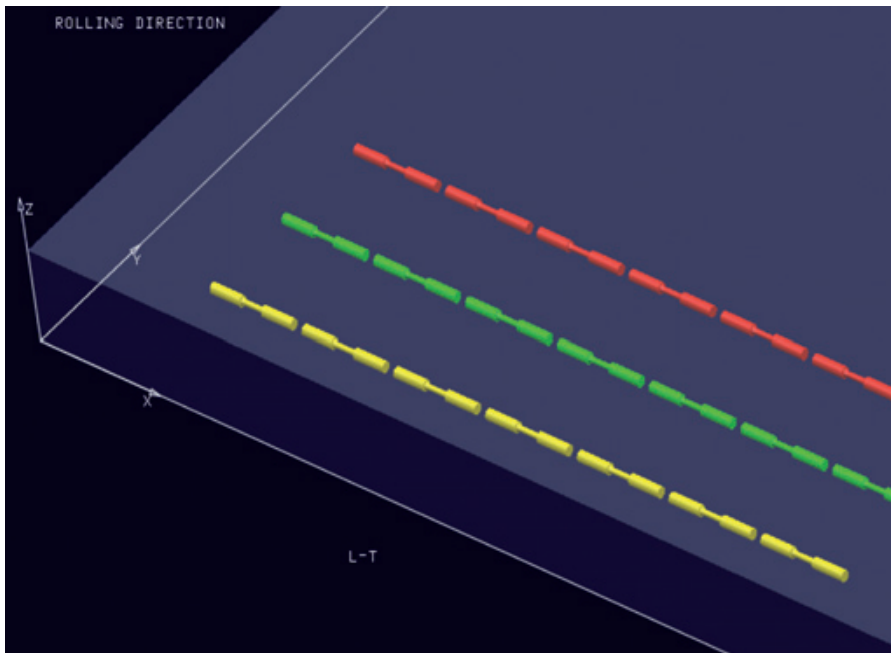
Esquema de extracción de probetas para ensayos de corrosión bajo tensiones
